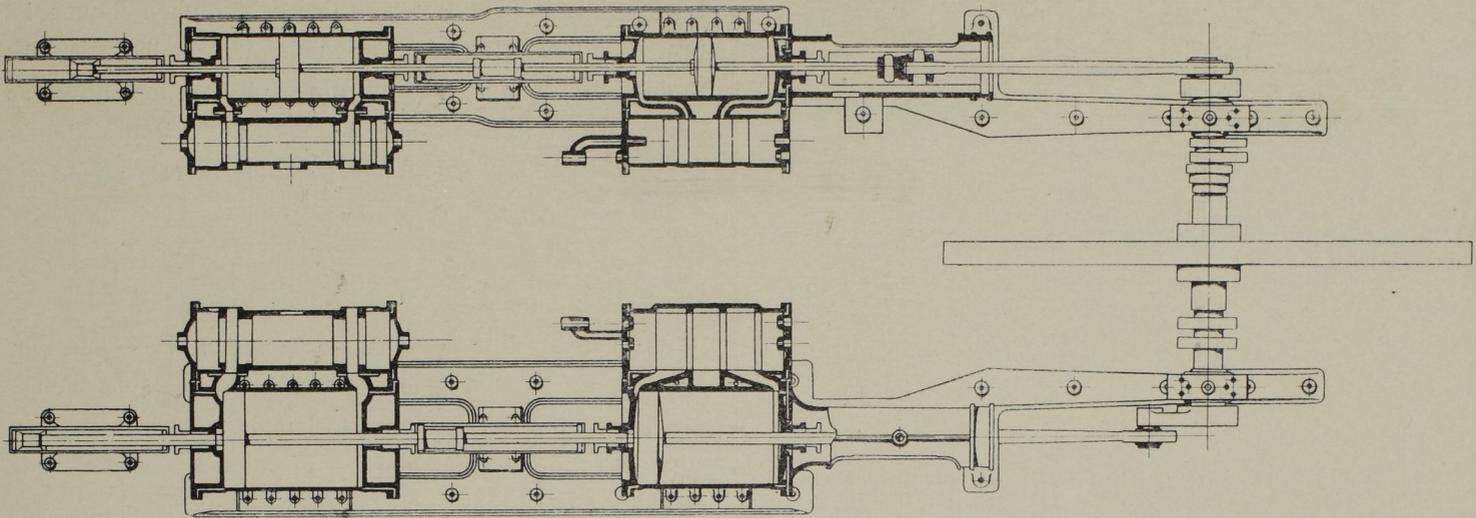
Grundriss. Masst. 1 : 80.
